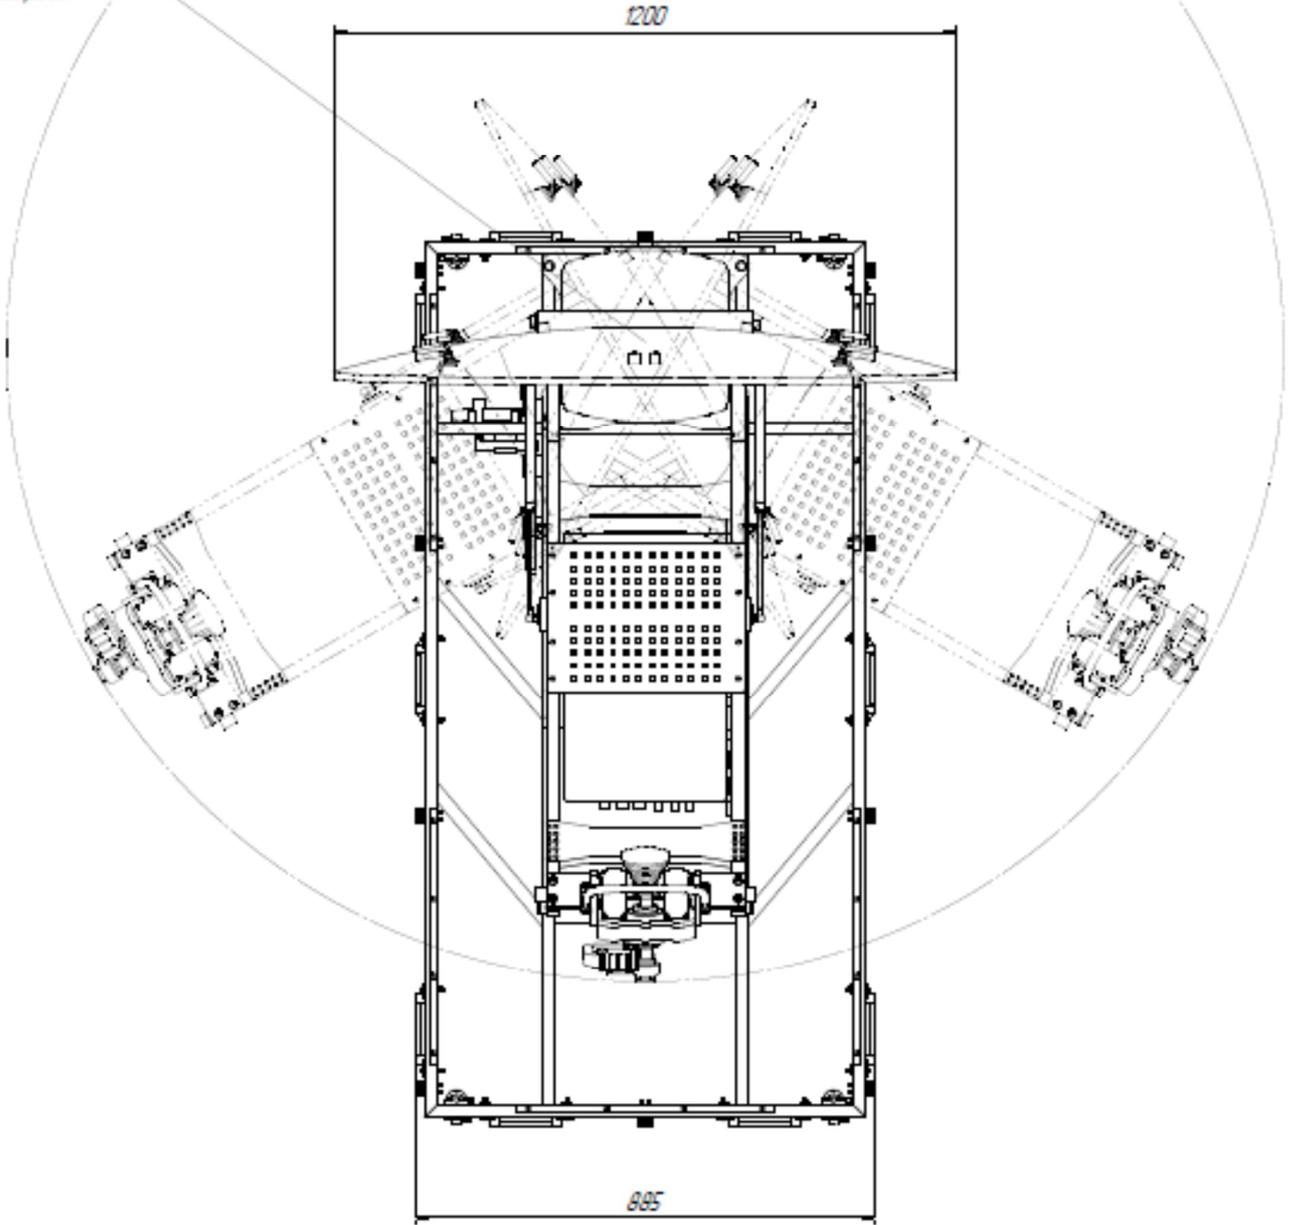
Габаритные размеры ЗССС 1,2 м
